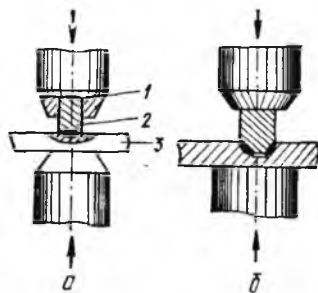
Схемы сварки длинных штифтов с листами на точечных конденсаторных машинах.
